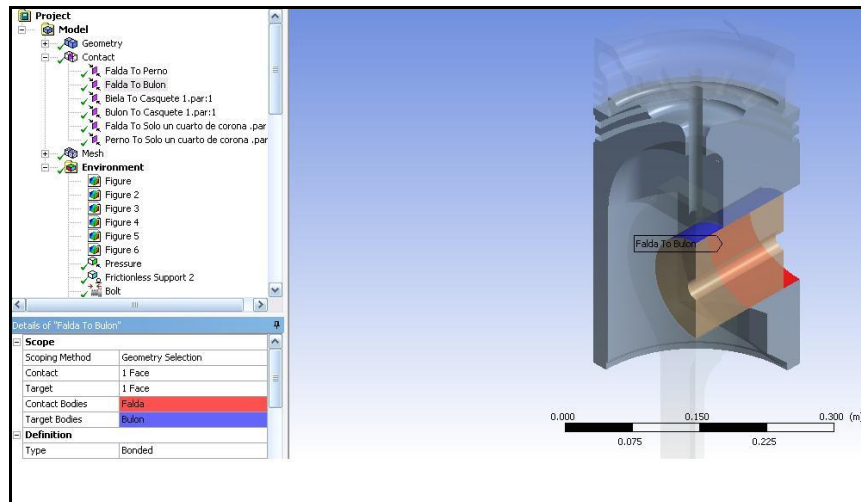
Contacto tipo soldado entre Falda - Bulón.
